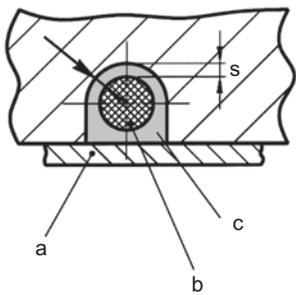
Eingebetteter Rohrheizkörper mit Abdeckung (z.B. Reflektorplatte)
